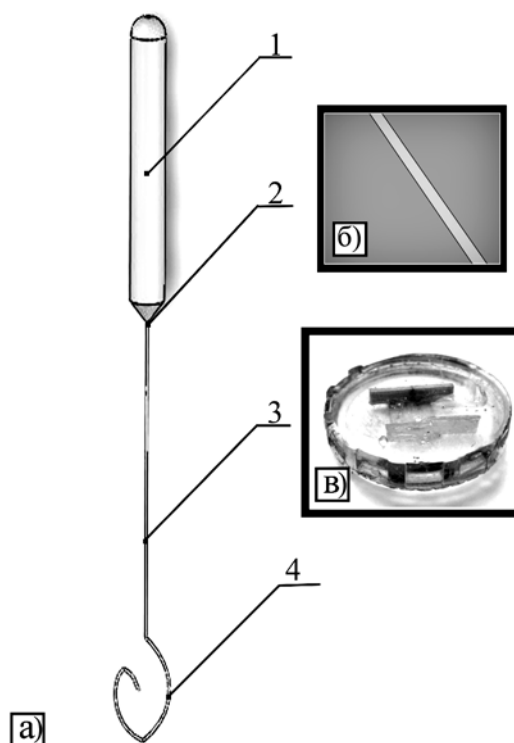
Чертеж ретрактора для мобилизации подкожных вен (а): 1 – рукоятка; 2 – сварной шов; 3 – стержень; 4 – крючок; условное увеличенное изображение сварного шва, выполненного ИК-сваркой (б); шлиф образца для исследования сварного шва (в)
